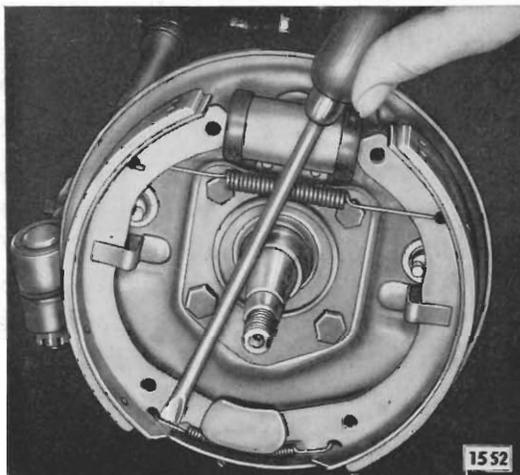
Untere Rückzugfeder aus Bremsbacke aushängen
